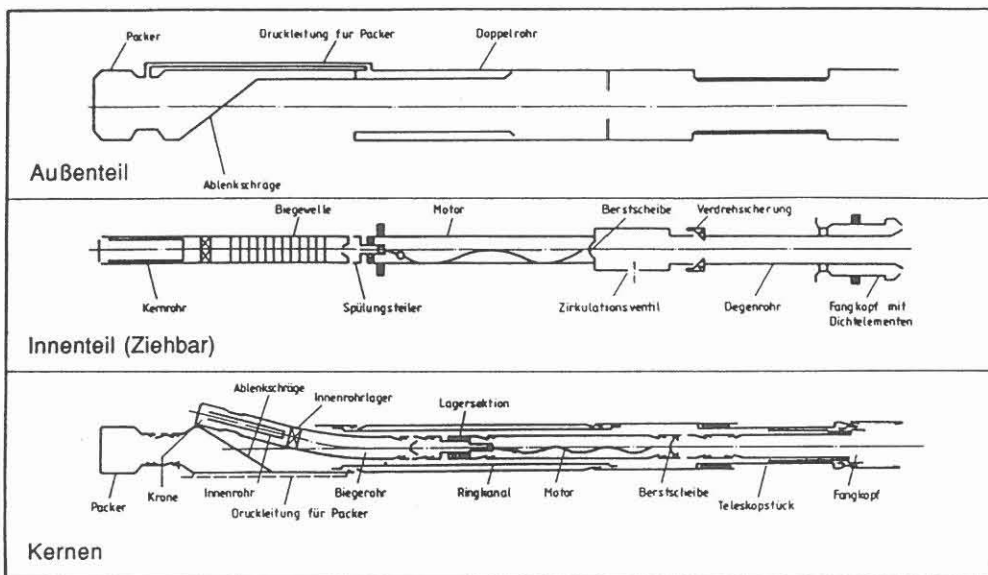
Im Laboratorium getestetes Prinzip eines Seitenkernbohrgerätes mit Ablenkschräge und Spülmotor (EC/ITE)
